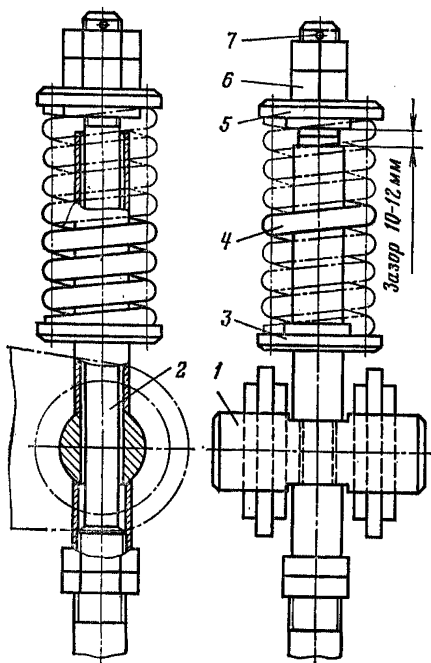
Пружинное звено исполнительного органа тормоза подъемных машин БМ-2000-3А и 2БМ-2000-3А:
